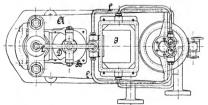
c. Schmiedepresse der Duisburger Maschinenbau-A.-G.
